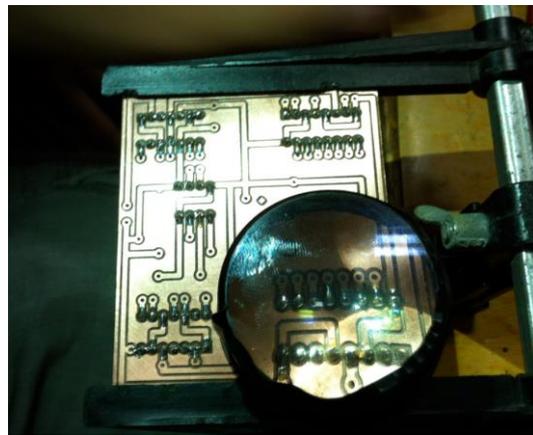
Aprendendo a soldar e fazer placa de circuito impresso
